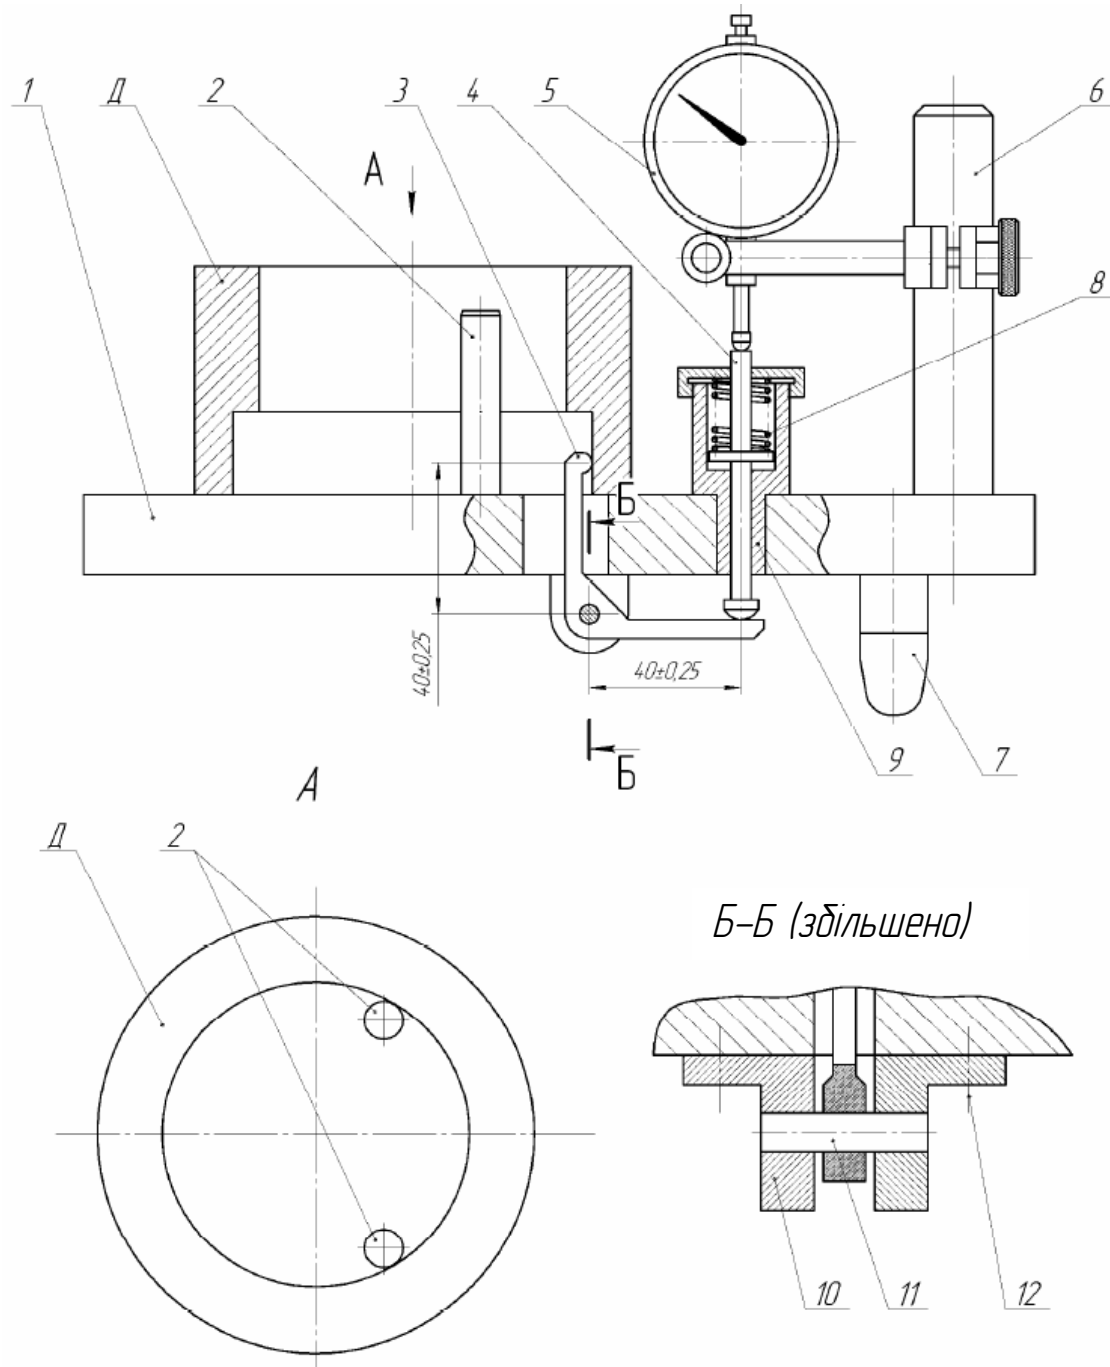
Пристосування для контролю радіального биття внутрішніх циліндричних поверхонь деталі
